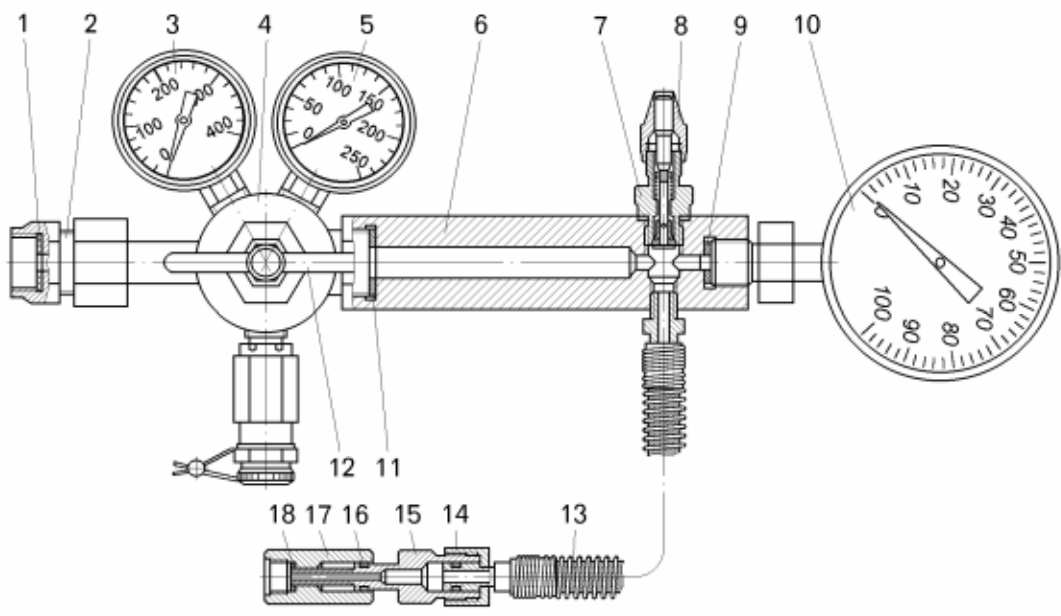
Приспособление для зарядки цилиндров подвески:
